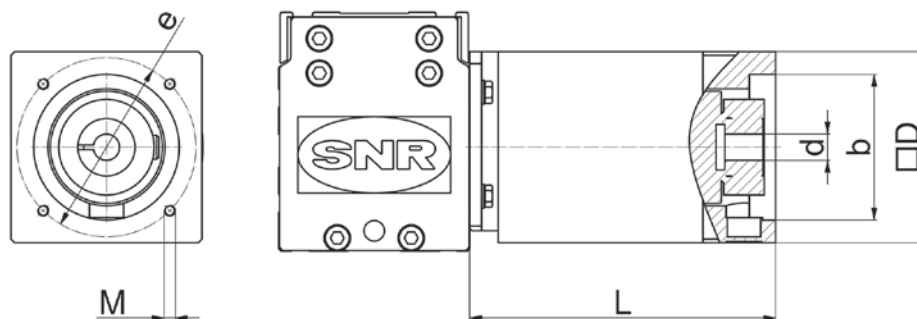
Abmessungen AXC mit steckbarem Planetengetriebe Variante ZS
